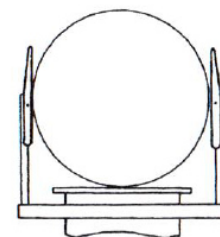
Транспортировка рулонов АП с боковыми гидравлическими захватами
